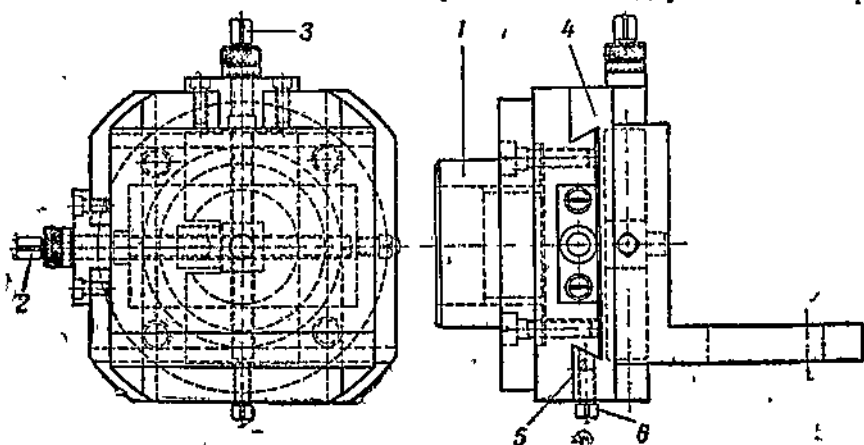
Шлифовальная головка для внутренней шлифовки
